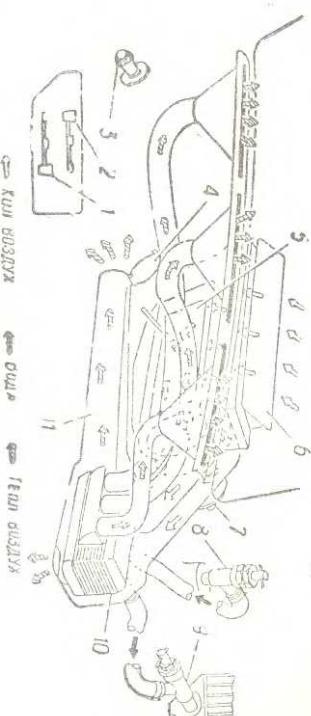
Отопление и вентиляция кабины и обдув ветрового стекла:
